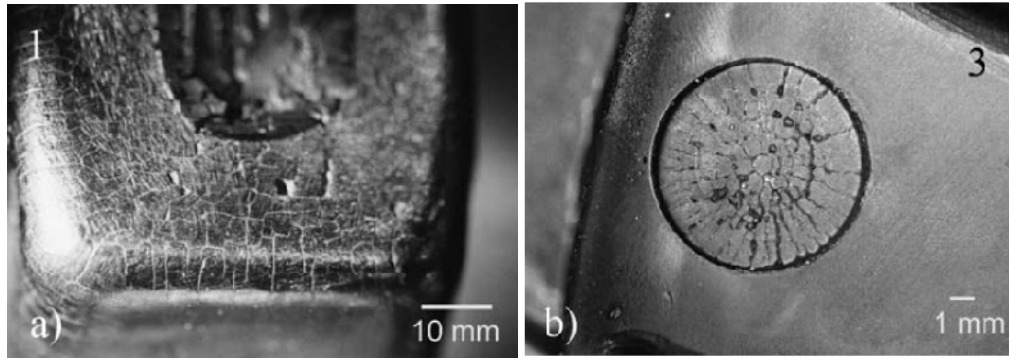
Agrietamiento reticular. a) herramienta para forjado en caliente, b) molde de fundición [3].
